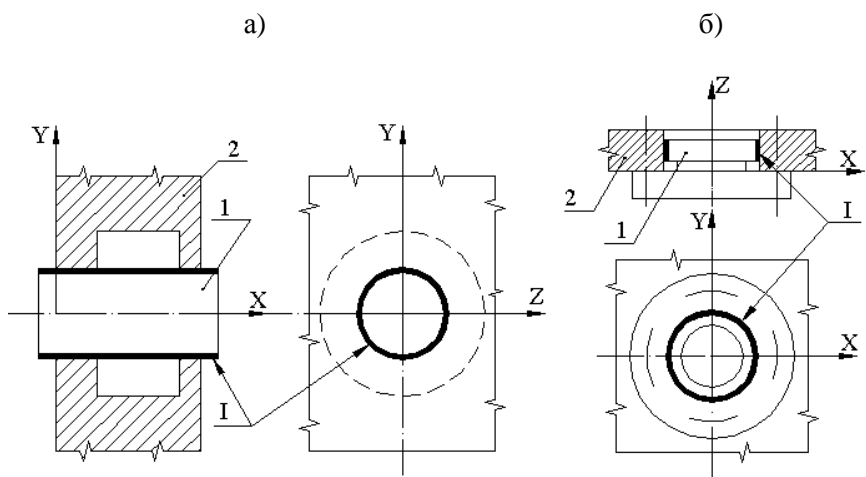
Базирование заготовок (деталей) с использованием цилиндрических базовых поверхностей:
